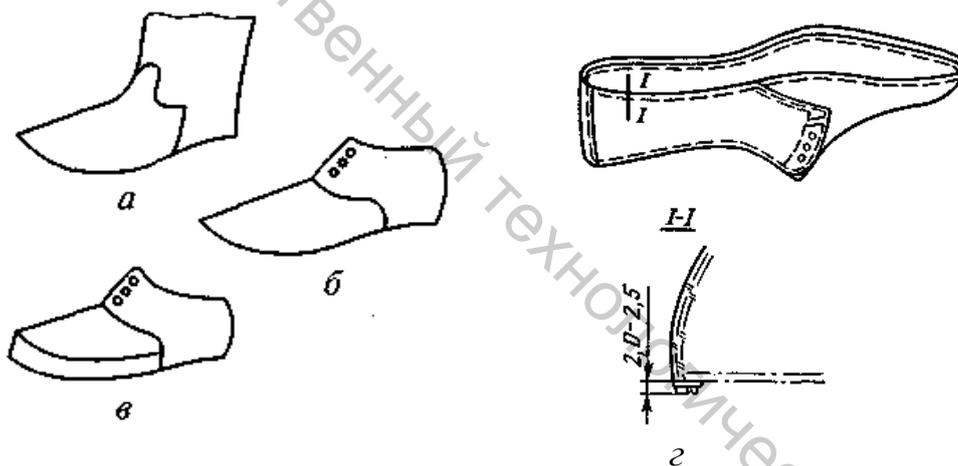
Конструкции заготовок по степени пространственности:
